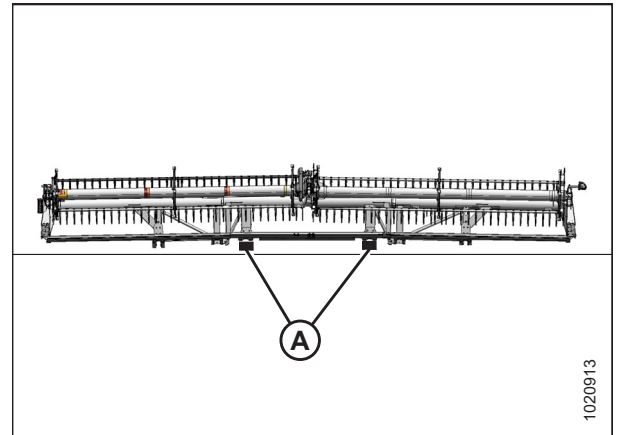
Розташування блоків FlexDraper® — жатки з подвійним мотовилом
